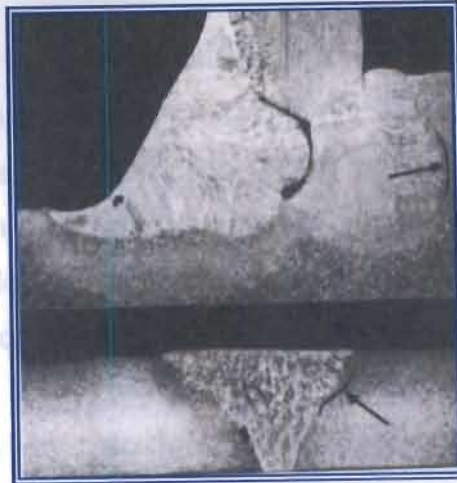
Ejemplo de agrietamiento bajo el cordón de soldadura ^[2].
